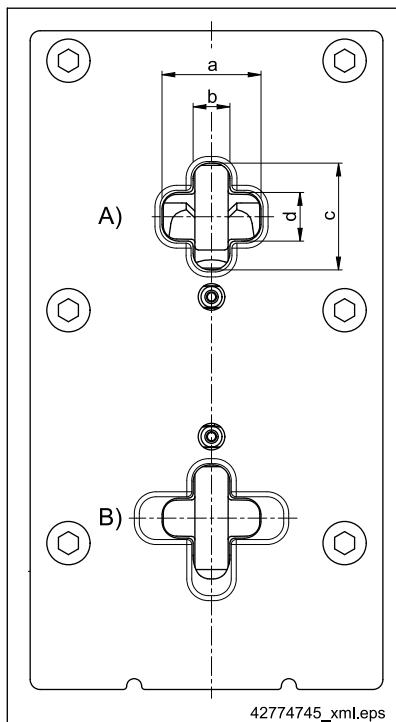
Lasthakenansicht (A), Kettenansicht (B)
